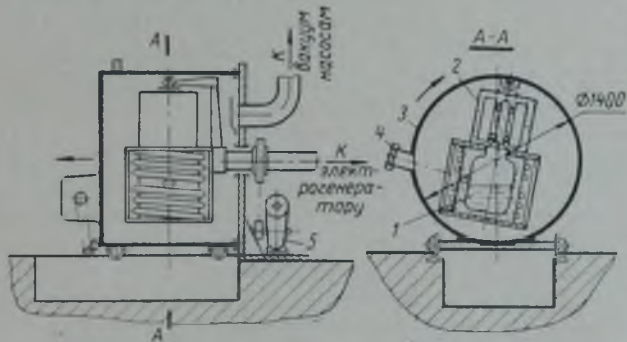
Схема вакуумной установки для плавки и заливки окисляющихся сплавов
